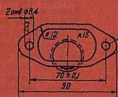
Двойной всасывающий патрубок для установки двух карбюраторов.
